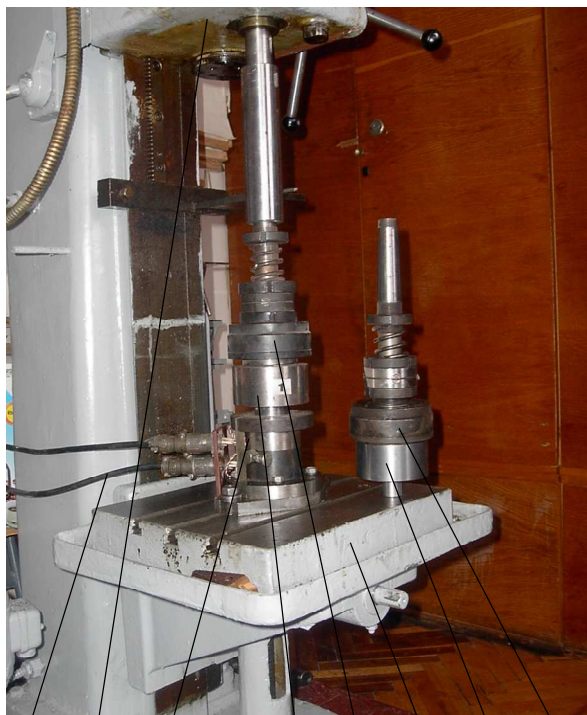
Експериментальна установка для розточування кільцевих канавок в отворах корпусних деталей.
